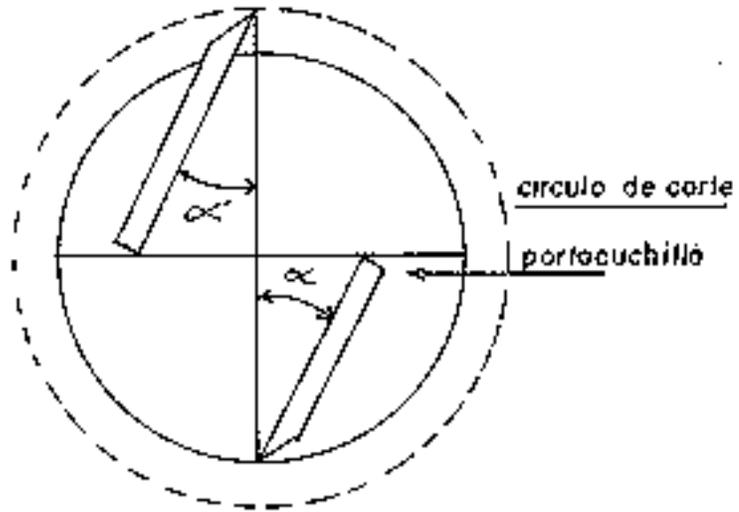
Ensayo de Moldurado en Cuchilla Sobresalida
